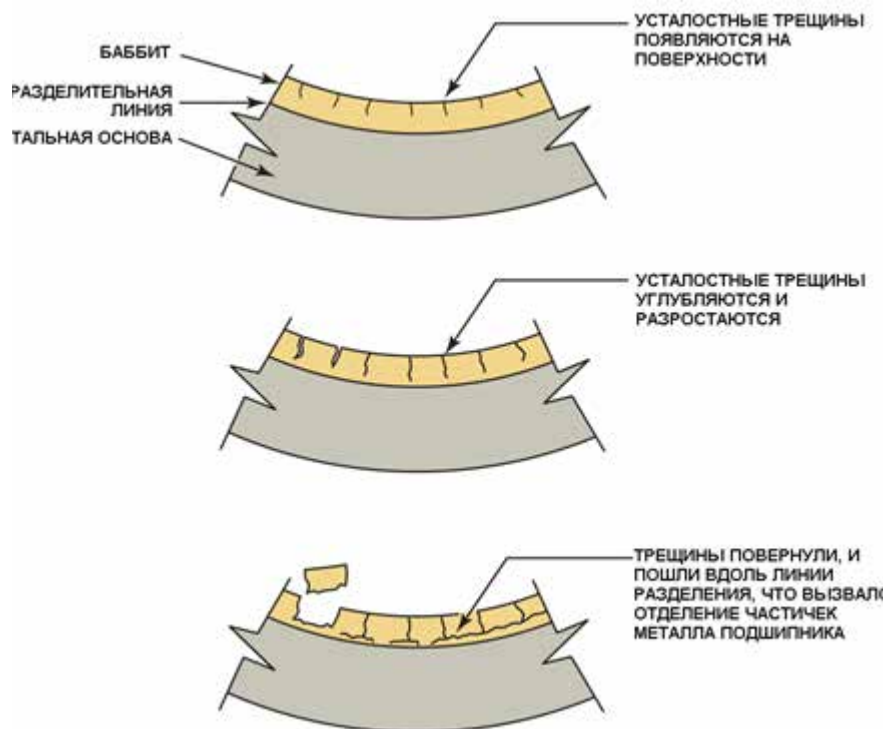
Затвердевший материал подшипника становится хрупким, и появляются трещины, постепенно разрушающие материал подшипника; источник: *Pearson Education, Inc.
